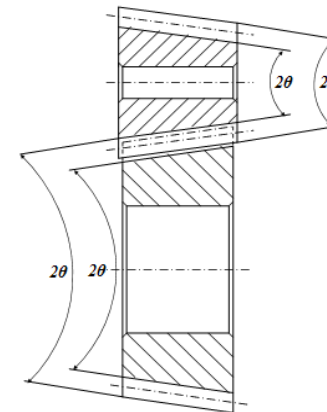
Схематичное изображение цилиндрической зубчатой пары Новикова со спрямленными зубьями
